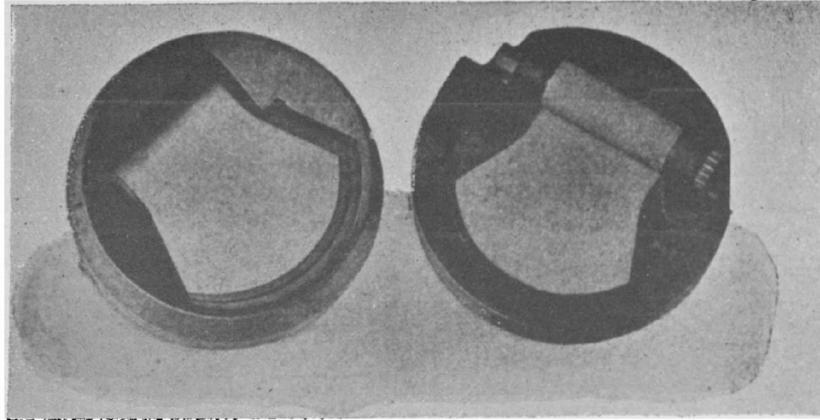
Clapets Gutermuth placés dans la boîte à soupapes (Type des compresseurs à SO² Borsig de Berlin-Tegel).
